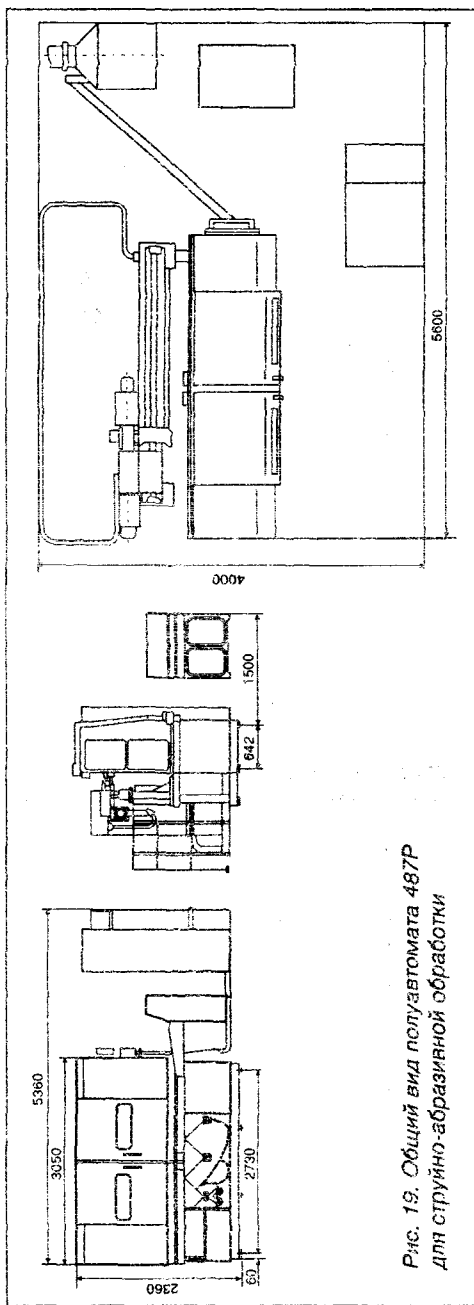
Общий вид полуавтомата 487Р для струйно-абразивной обработки
